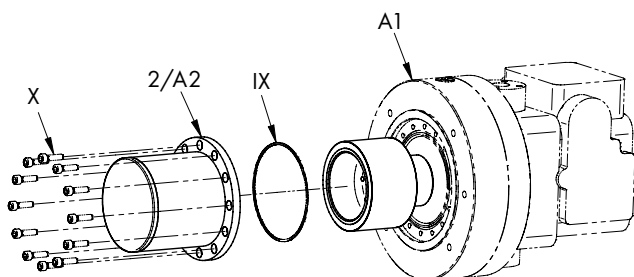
Assemblaggio/signatura di base del bicchiere sulla flangia per sistemi tecnicamente ermetici (A4)
